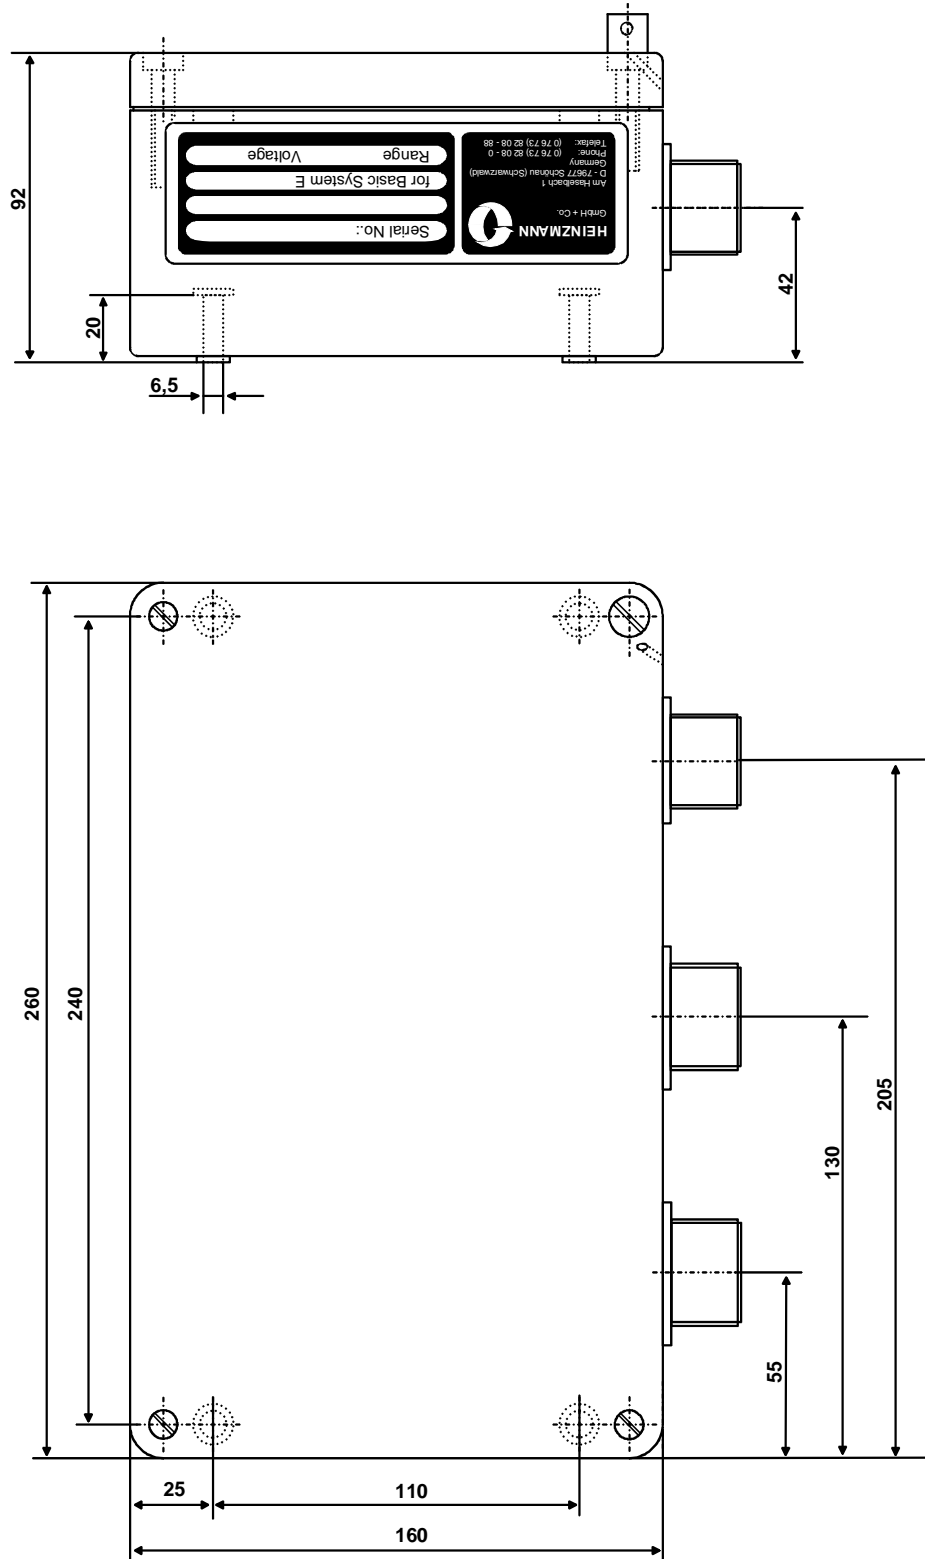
Gehäuse von DC EDC 2 - 01 - 55
